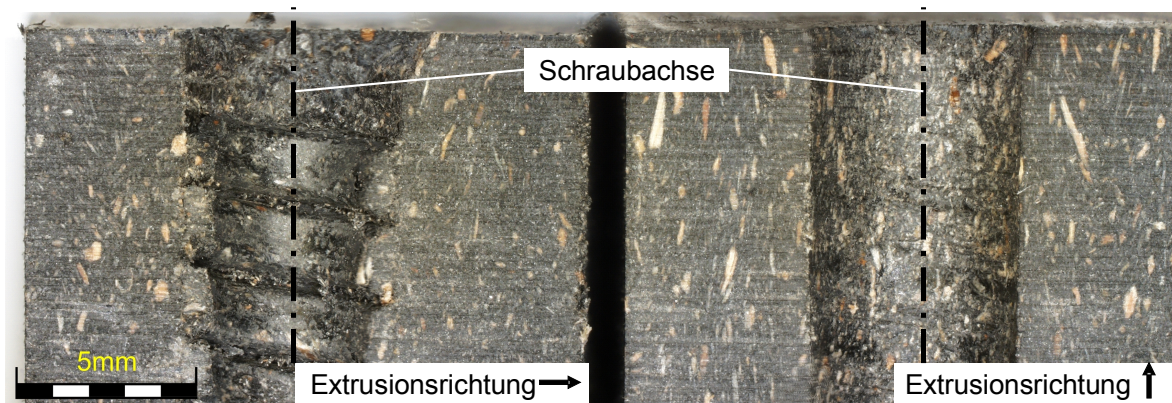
Gewindeeingriff nach dem Versagen im Überdrehversuch für die Einschraubrichtung senkrecht zur Extrusionsrichtung S-SE (links) und parallel zur Extrusionsrichtung S-PE (rechts), Werkstoff WPC-6, Schraube STS plus $d_1 = 6 \text{ mm}$, $d_K = 5 \text{ mm}$
